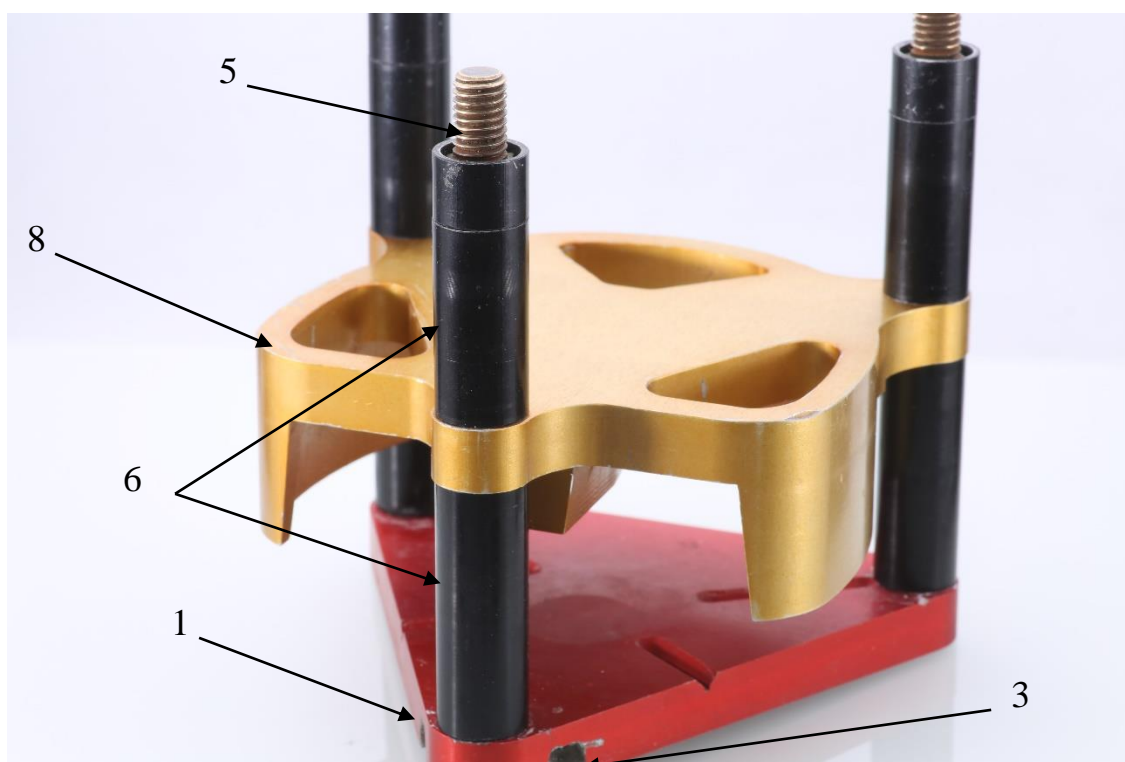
Устройство для изготовления зубных протезов с дополнительной платформой
